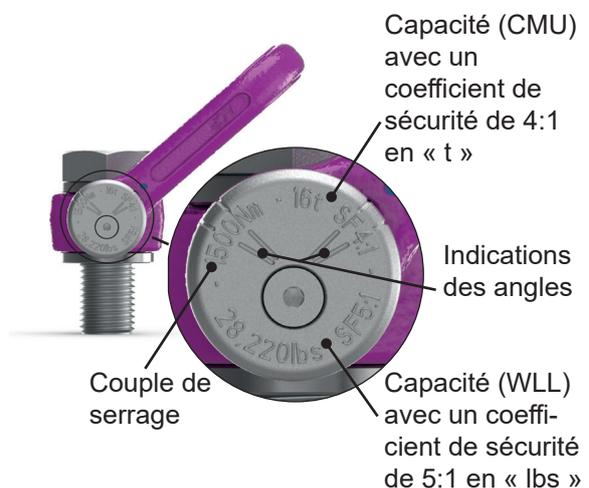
ACP M36-M100 ou 1 1/2"-4" - Indications sur le disque latéral
